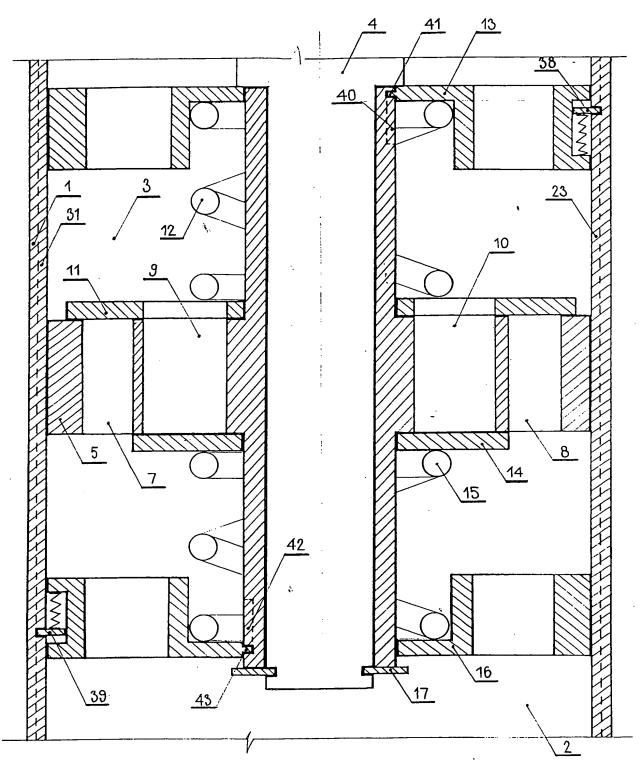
Развертка внутренней поверхности детали (1) устройства, изображенного на фиг.4.
